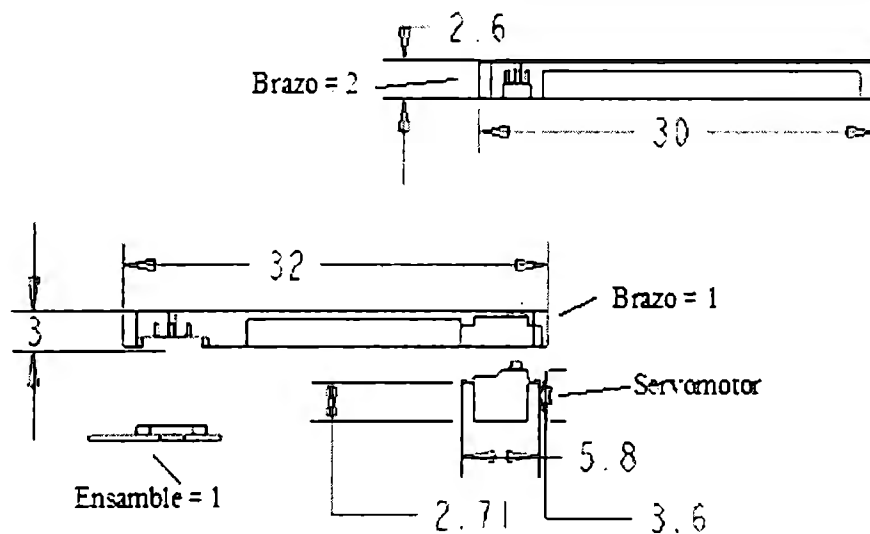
Diseño de los brazos del sistema en ProE®. Las dimensiones están en cm.
